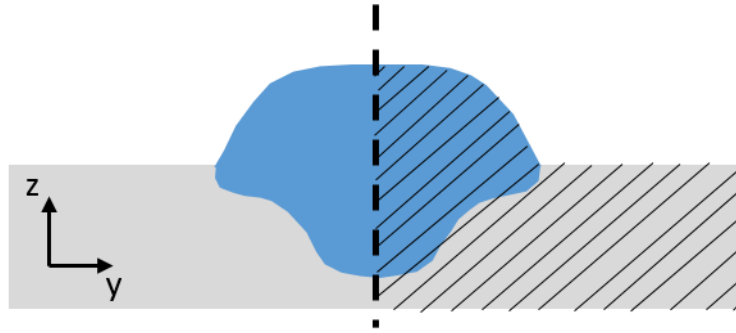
COUPE TRANSVERSALE D'UNE PIÈCE ET PLAN DE SYMÉTRIE LONGITUDINAL
